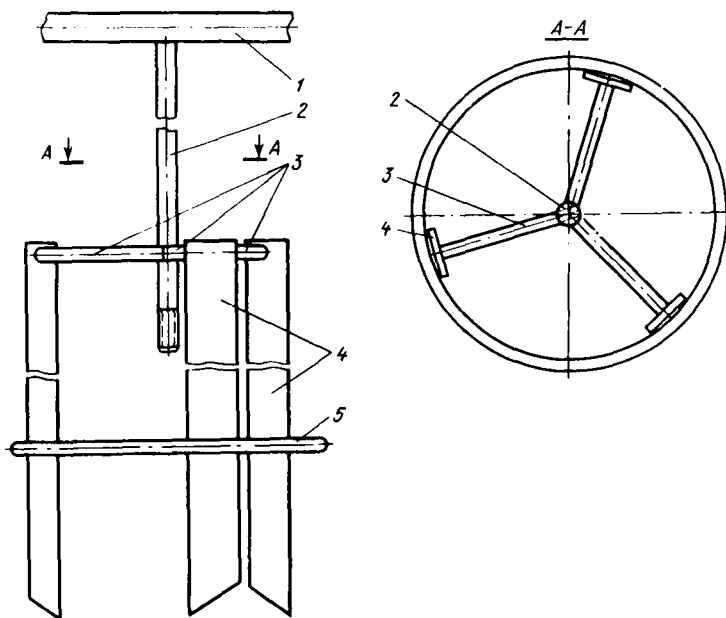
Поворотный узел трехножевого устройства для обрезки кустов земляники:
